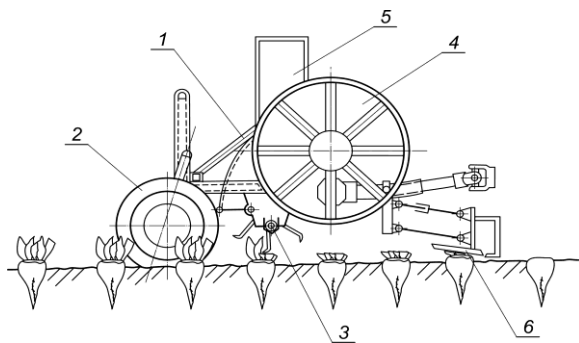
Конструктивно-технологічна схема: 1 – рама; 2 – пневматичні копіювальні колеса; 3 – роторний гичкорізальний апарат; 4 – гвинтовий транспортер та лопатева шпурлялка; 5 – завантажувальна труба; 6 – дообрізувач головок коренеплодів.
